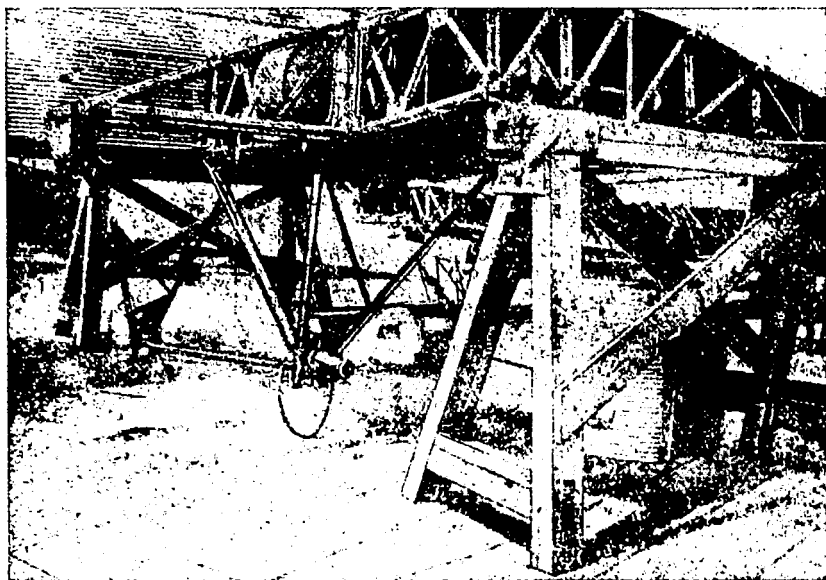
Установка низких козелков с мягкой обивкой, допускающих монтаж шасси, но без постановки колес.
